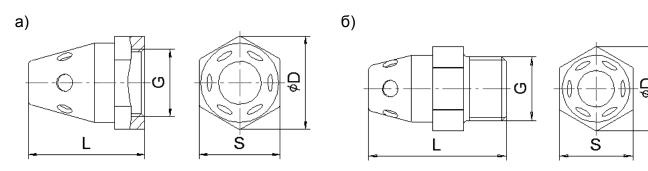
Общий вид газовых распылителей: а) с внутренний резьбой; б) с наружной резьбой
